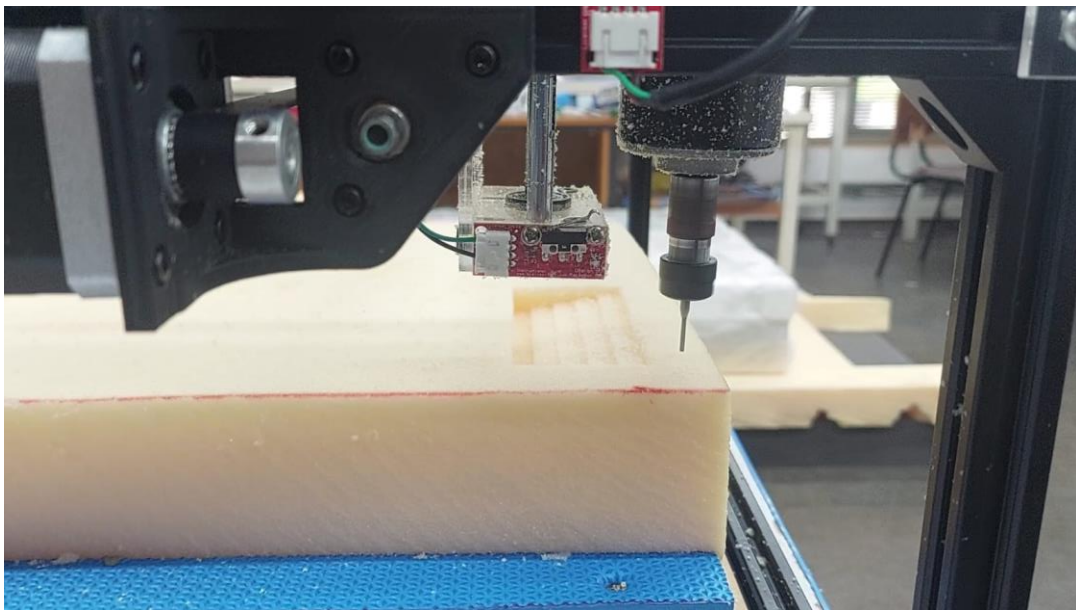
Processo de usinagem por desbaste realizado na máquina CNC
